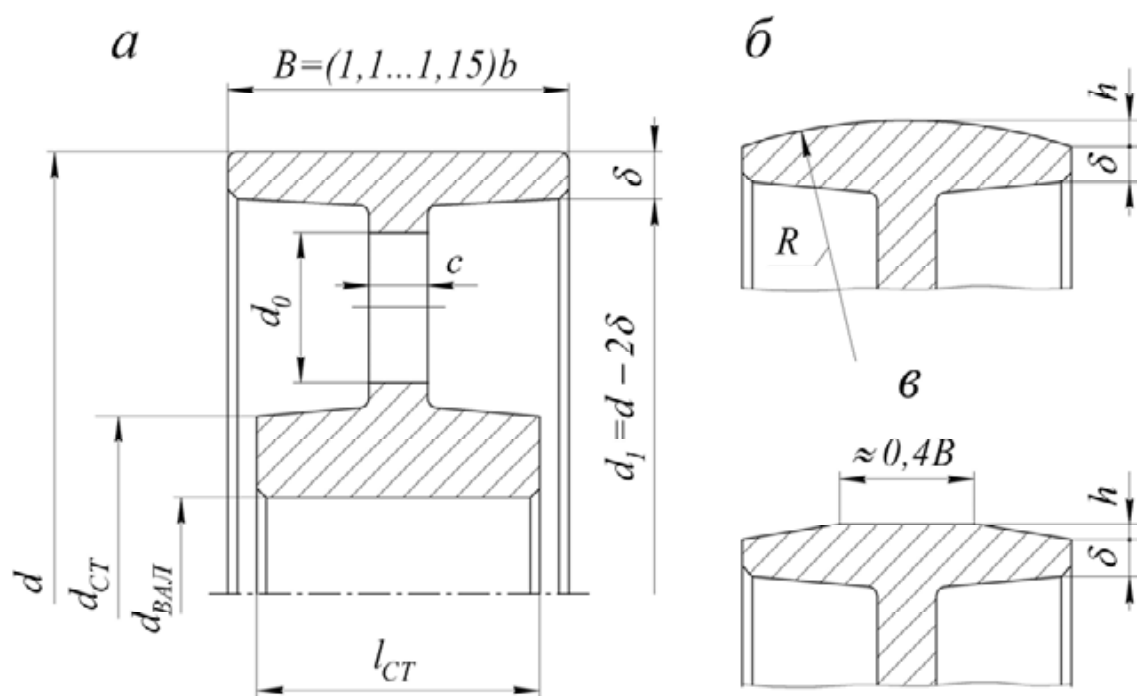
Шкив плоскоременной передачи: *а* – конструкция шкива; *б* – сферическая форма обода шкива; *в* – с двумя конусами
